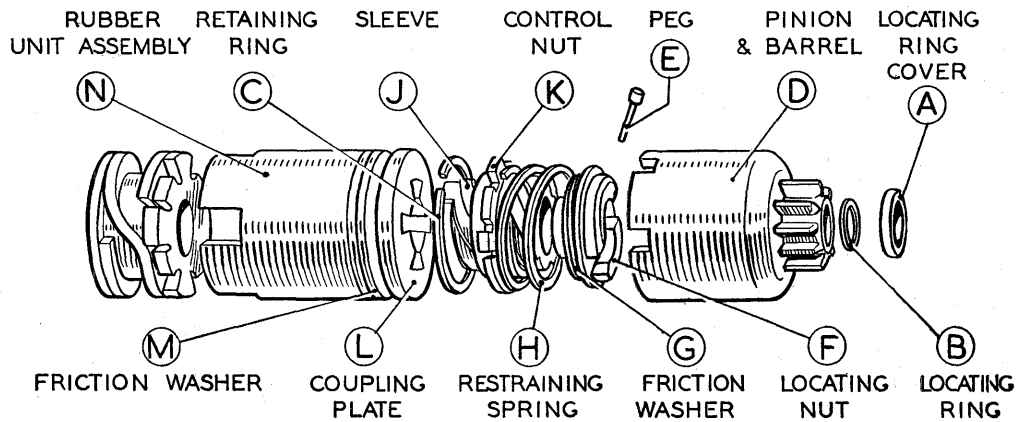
Starterdrev type RSB i exploded-view. (Den ved E viste stift findes ikke på nyere udførelser, hvor styremøtrikken er stemmet på. Ved eventuel adskillelse må en ny møtrik monteres).
